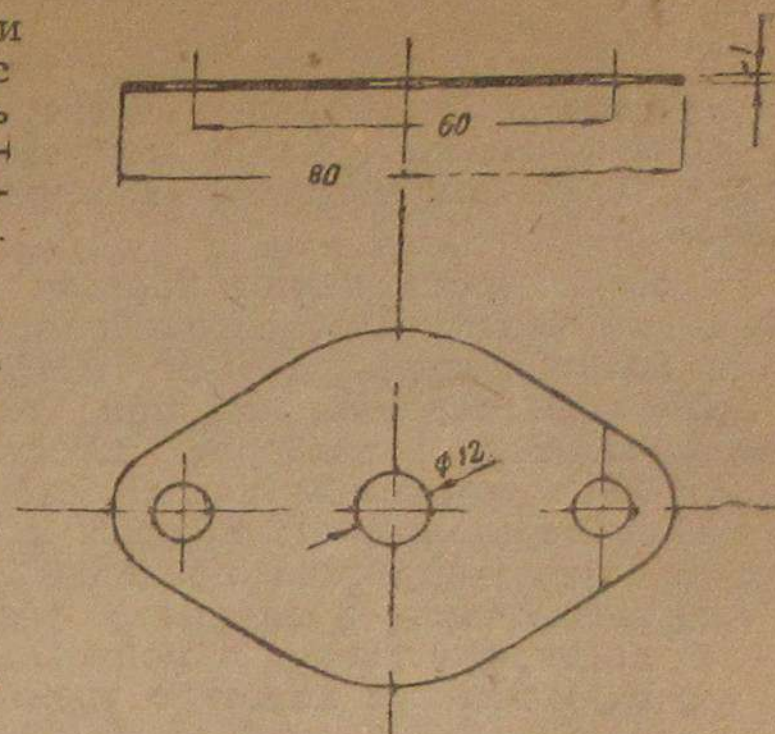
Шайба к карбюратору для уменьшения числа оборотов двигателя.
